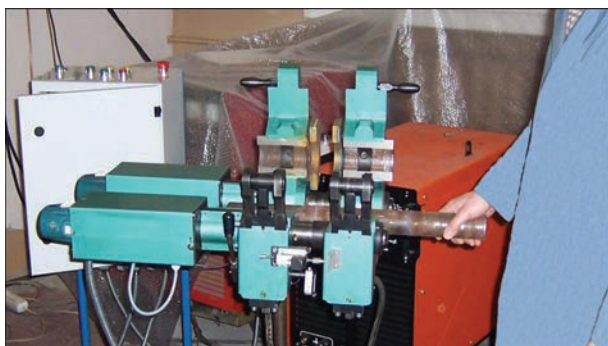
Установка труб в зажимные устройства сварочной машины
